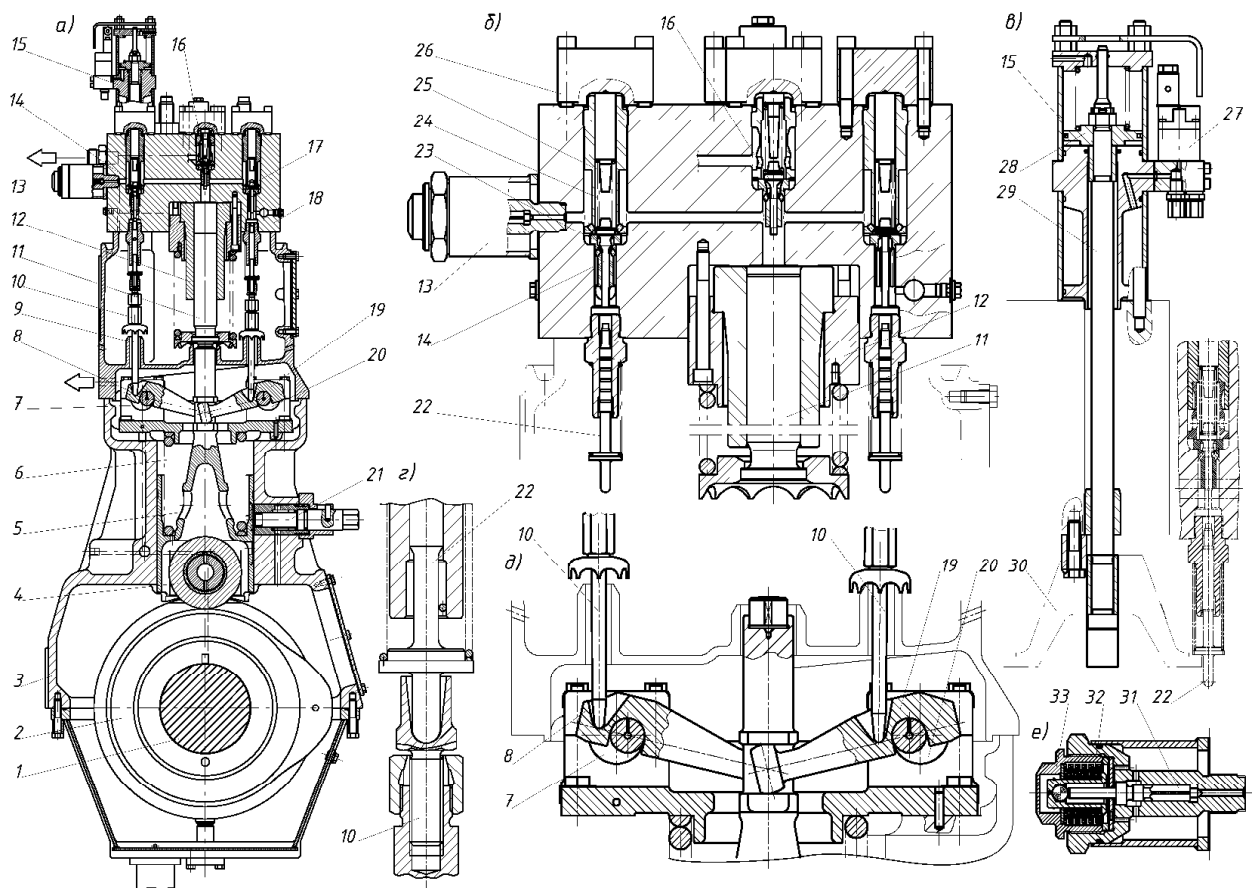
Секція високого тиску із клапанним керуванням подачею дизеля RTA72 фірми Wartsila і її елементи. а – загальний вигляд ПНВТ; б – кришка насоса із клапанами; в – механізм аварійної зупинки двигуна; г – штанга штовхача привода клапанів; д – механізм привода клапанів; е – запобіжний клапан. 1 – вал блоку насосів; 2 – кулачок приводи плунжера; 3 – корпус насоса; 4 – ролик штовхача; 5 – штовхач; 6 – зворотня пружина; 7 – ексцентриковий вал важелів привода наповнювальних клапанів; 8 – важіль привода наповнювального клапана; 9 – штанга штовхача; 10 – механізм регулювання зазорів у приводі клапана; 11 – плунжер; 12 – втулка плунжера; 13 – запобіжний клапан; 14 – наповнювальний клапан; 15 – механізм аварійного відключення подачі палива; 16 – нагнітальний клапан; 17 – відсічної клапан; 18 – кришка насоса; 19 – важіль привода зливального клапана; 20 – ексцентриковий вал важелів привода зливальних клапанів; 21 – устрій фіксації штовхача; 22 – штовхач клапана; 23 – сидло клапана; 24 – зворотна пружина клапана; 25 – упор клапана; 26 – кришка клапанного колодязя; 27 – механізм керування клапаном аварійної зупинки; 28 – пневматичний поршень механізму аварійної зупинки; 29 – шток механізму аварійної зупинки; 30 – траверсу підйому наповнювальних клапанів; 31 – голка запобіжного клапана; 32 – тарілчаста пружина запобіжного клапана; 33 – регулювальний ковпак запобіжного клапана
